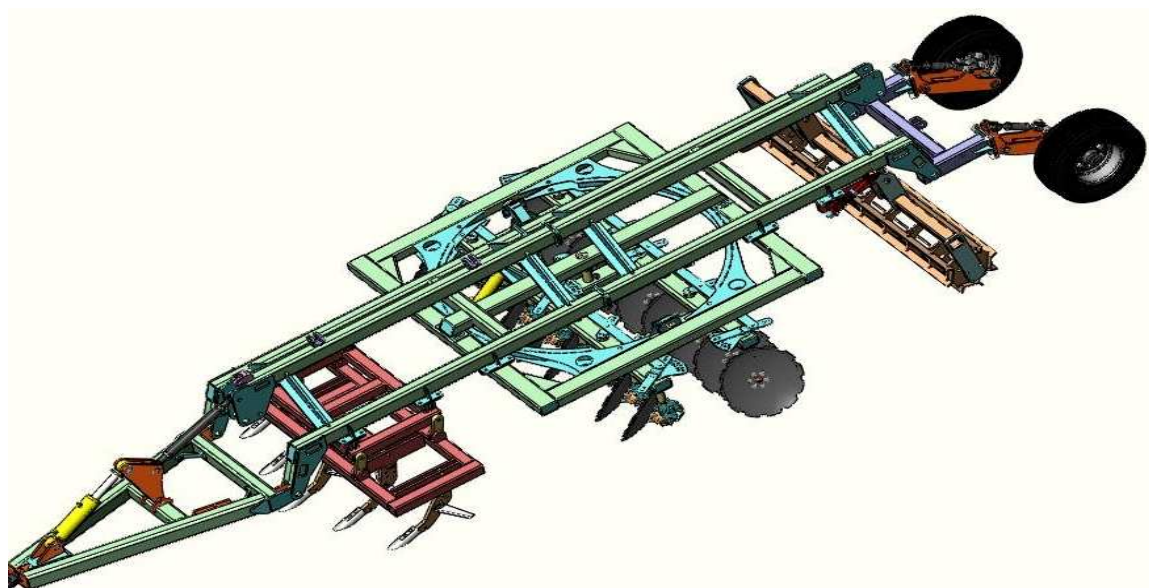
Агрегат почвообрабатывающий универсальный АПУ-1 в сборе – отладка (режим дискатора)
